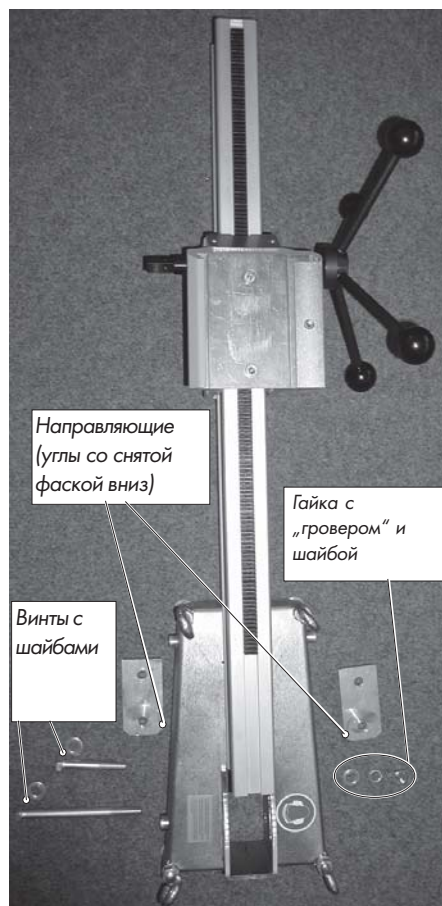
Универсальный сверлильный стоек с крепежом для Н•201-Uni-дюбельной подножки
